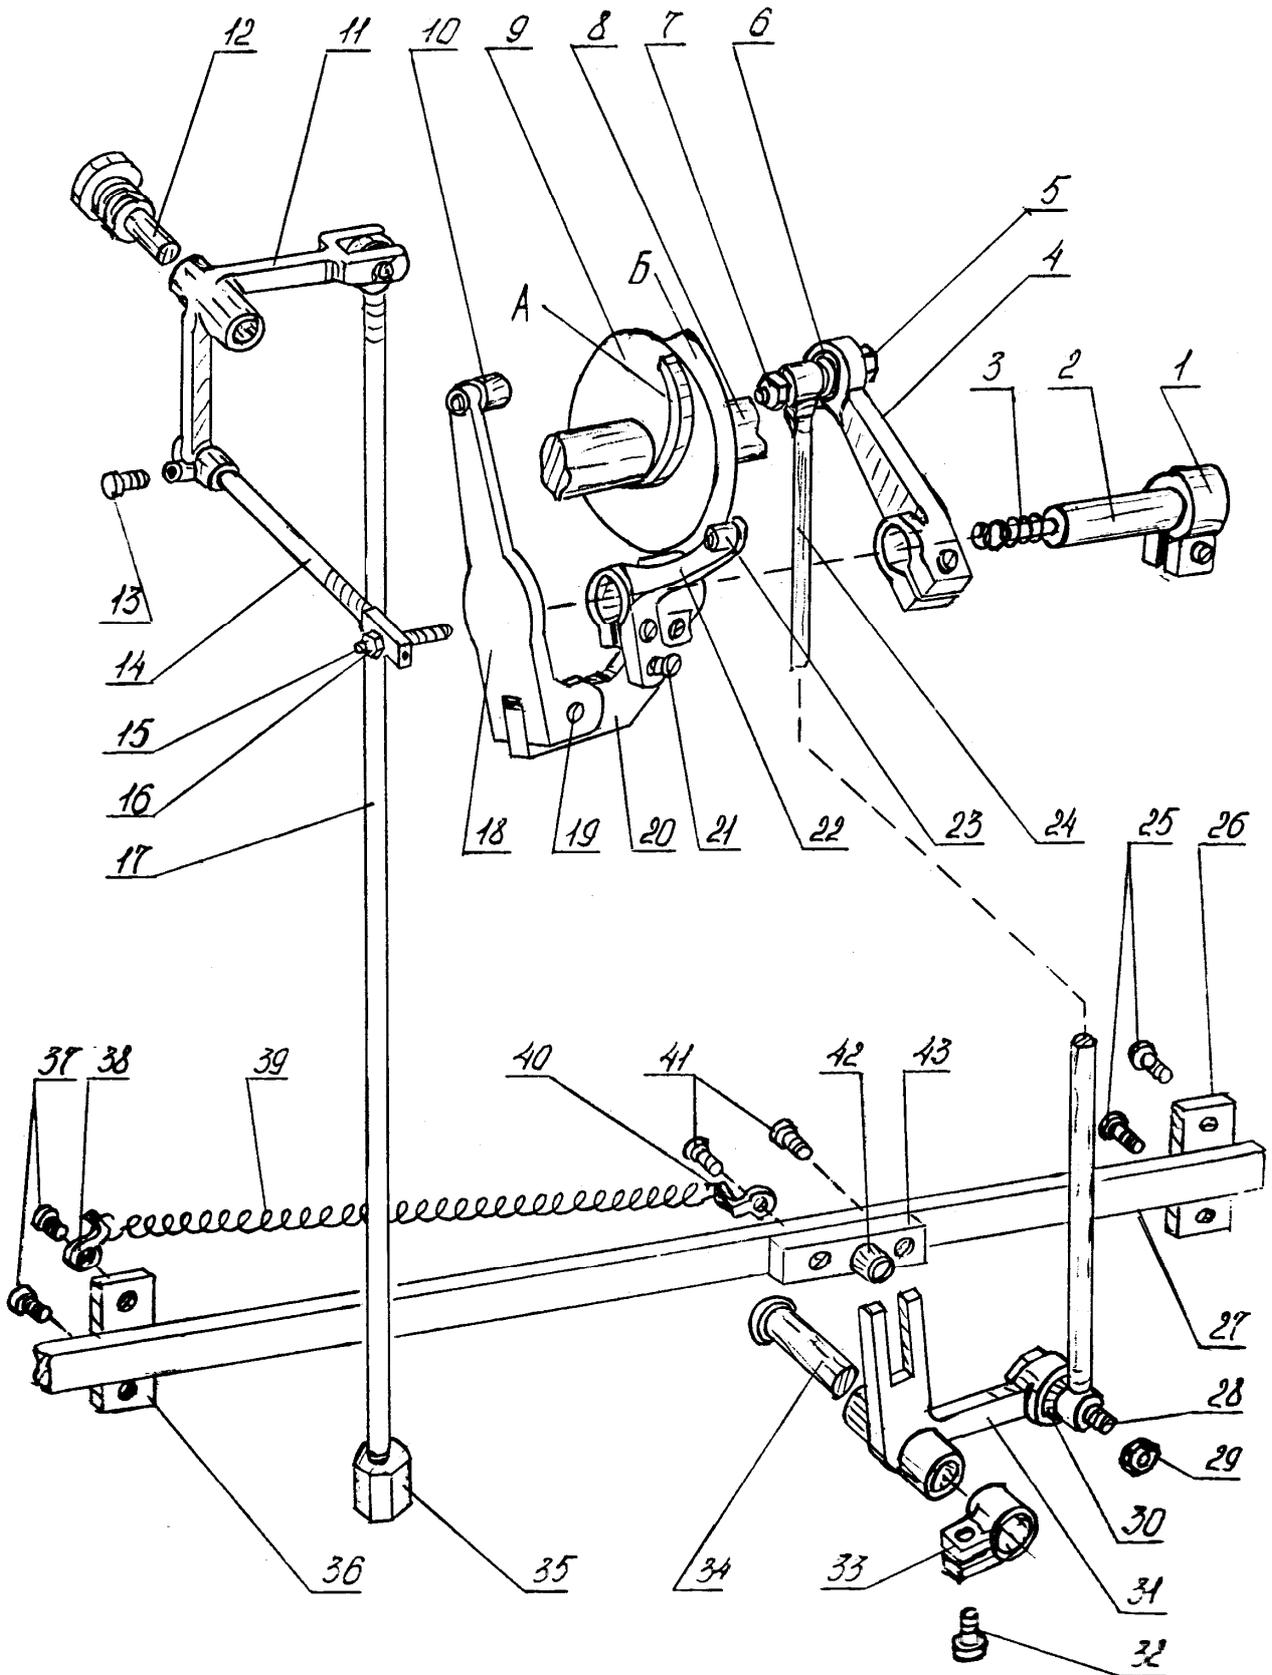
Механизм обрезки нитей. Устройство включения
